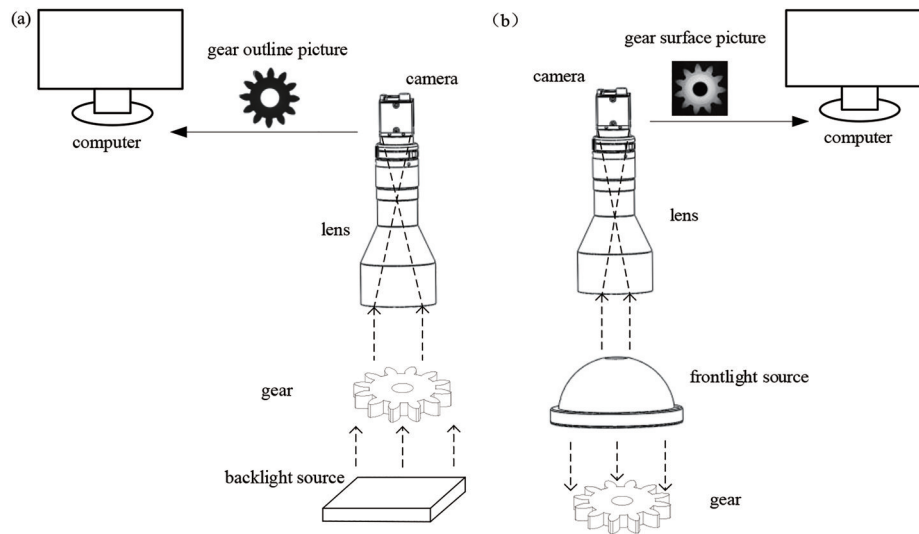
齿轮视觉检测仪器构成。(a) 齿轮精度测量系统;(b) 齿轮缺陷检测系统
